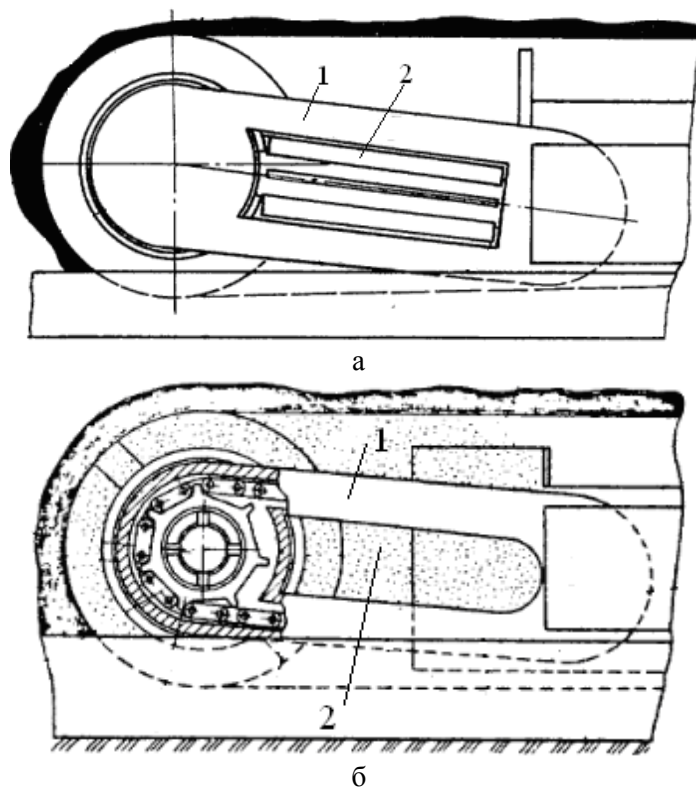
Общий вид поворотного редуктора очистного комбайна:
